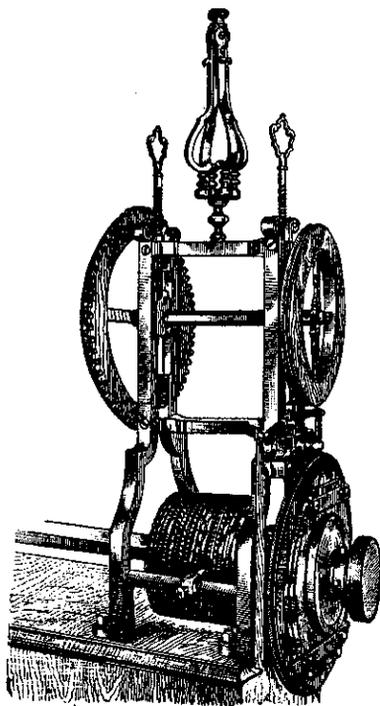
Гильоширный токарно-овальерный станок Нартова 1722 г. (общий вид).
